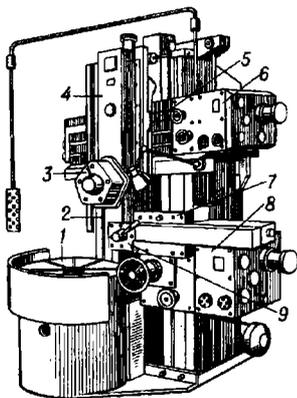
Токарно-карусельный станок: 1 – планшайба; 2 – станина с вертикальными направляющими; 3 – револьверная головка; 4 – вертикальный суппорт; 5 – поперечина; 6 и 8 – коробки подачи вертикального и бокового суппортов; 7 – боковой суппорт; 9 – резцедержатель
